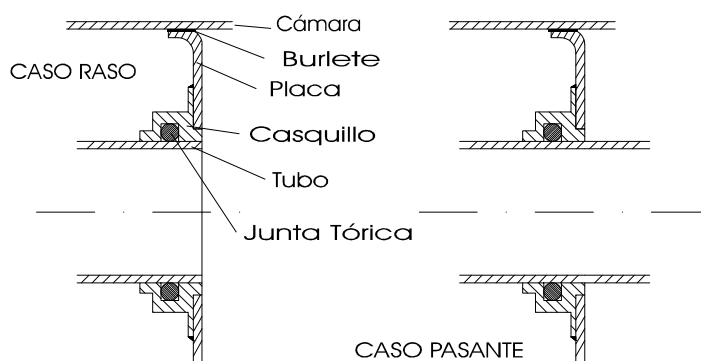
Esquema del montaje tubo-casquillo-placa.
